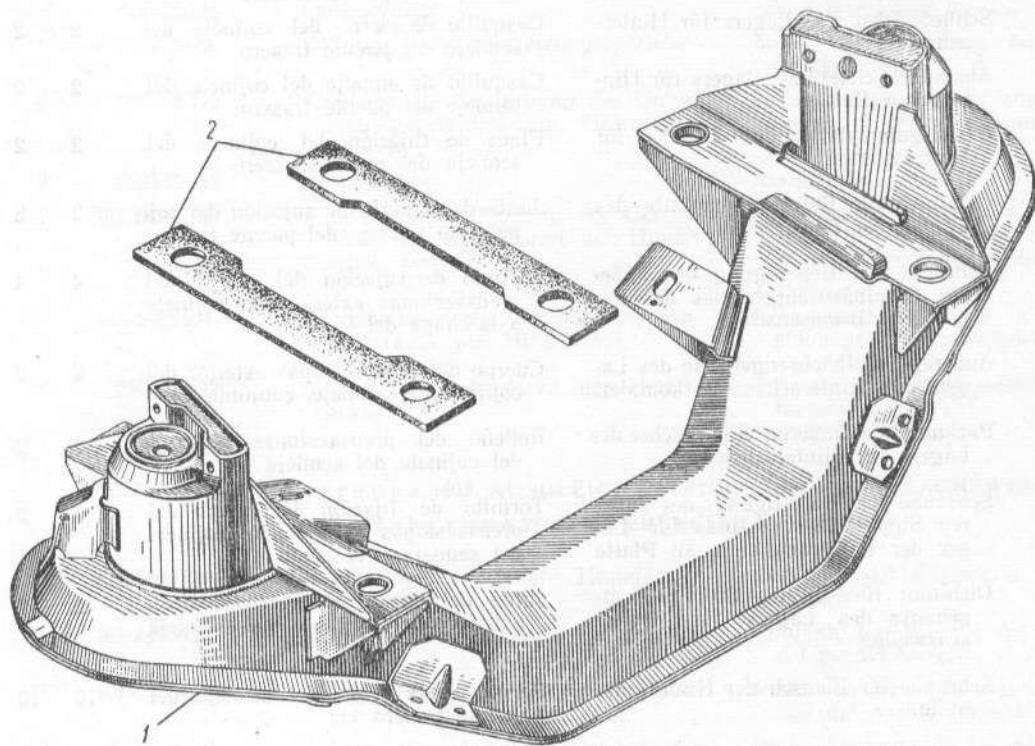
Querträger Nr. 2 mit Befestigungsteilen
